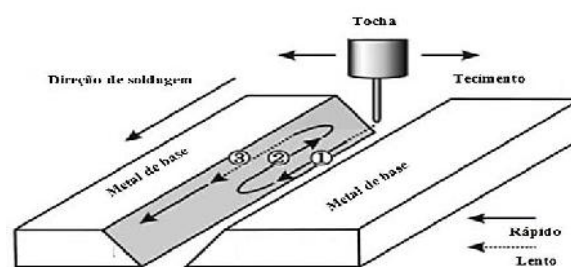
Oscilação triangular da tocha de soldagem durante a operação
